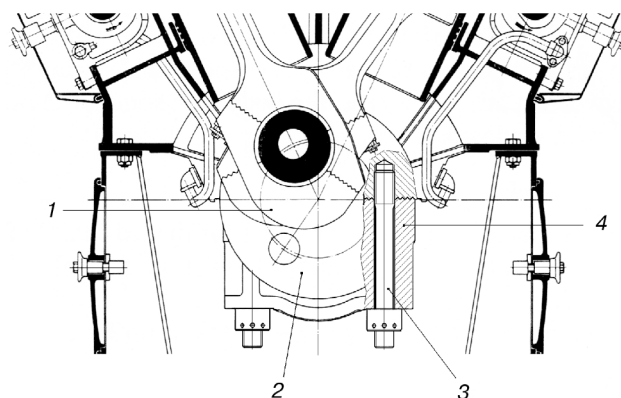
Подвеска коленчатого вала дизеля Sulzer 16-LVA24: 1 — шатун; 2 — коленчатый вал; 3 — шпилька; 4 — подвеска с зубчатым разъемом
